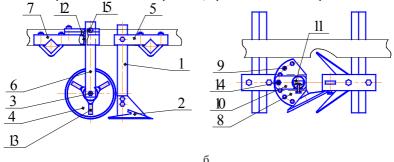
Рабочий орган культиватора: а) вид сбоку; б) вид сверху 1 и 6 – стойка; 2 – стрельчатая лапа; 3 – ось диска; 4 – диск сферический; 5 и 7 – кронштейн; 8 – пластина; 9 и 13 – отверстия; 10 – брус; 11 – паз; 12 – втулка; 14 и 15 – болт;
